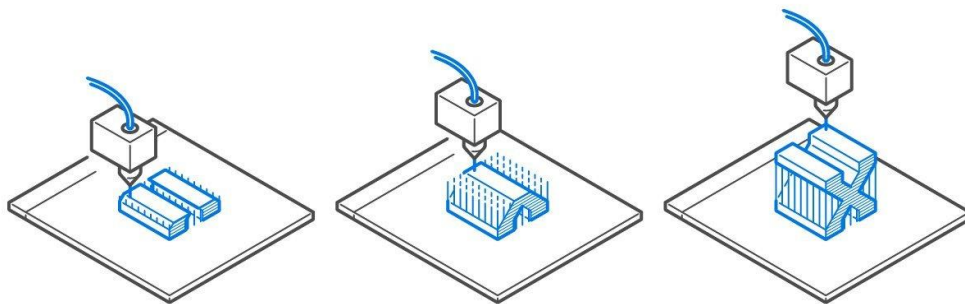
Técnica de impresión 3D por extrusión de material. [23]
